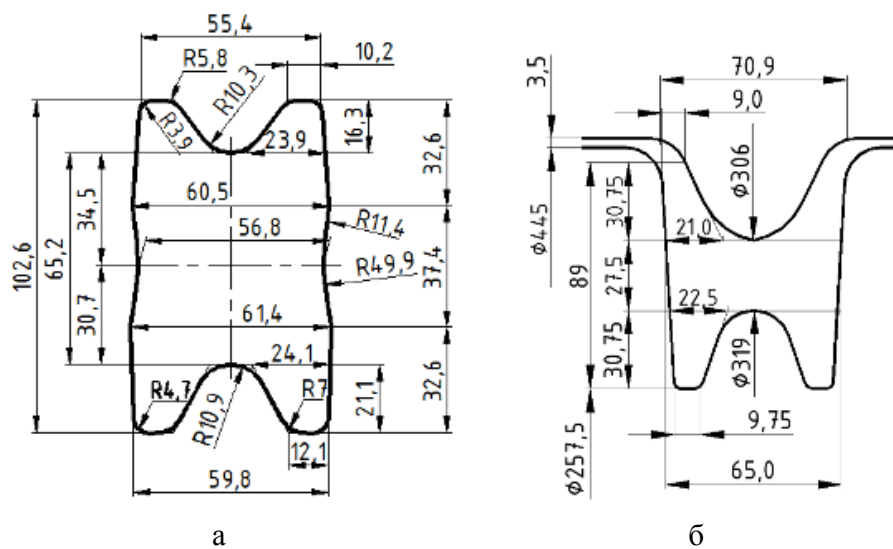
Вихідна заготовка (а) і чорновий закритий балковий калібр (б)
